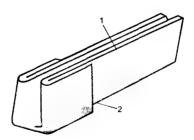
Внешний вид пазовой коробочки с манжетой для усиления: 1 — пазовая коробочка, 2 — отогнутая манжета
